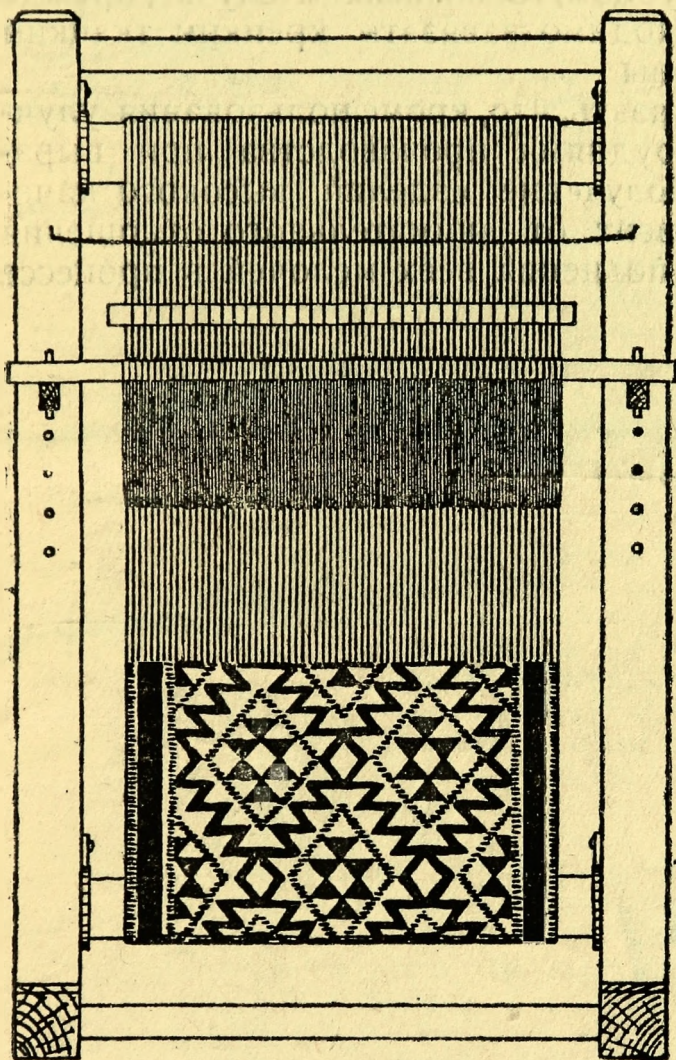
Ковровый станок для навивной основы с начатым ковром — вид спереди.
